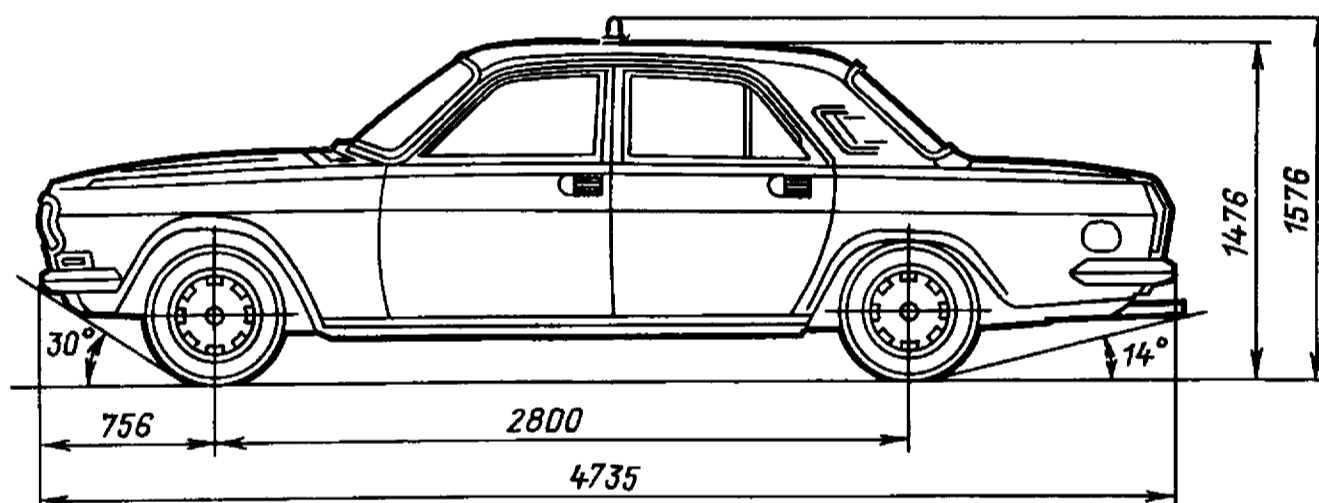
Автомобиль ГАЗ-24-11 «Волга» и его габаритные размеры
